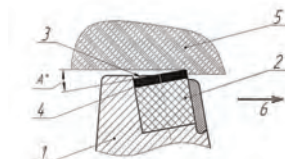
Принципиальная схема установки резца (Фиг. 1 из патента RU 190 616 U1)
